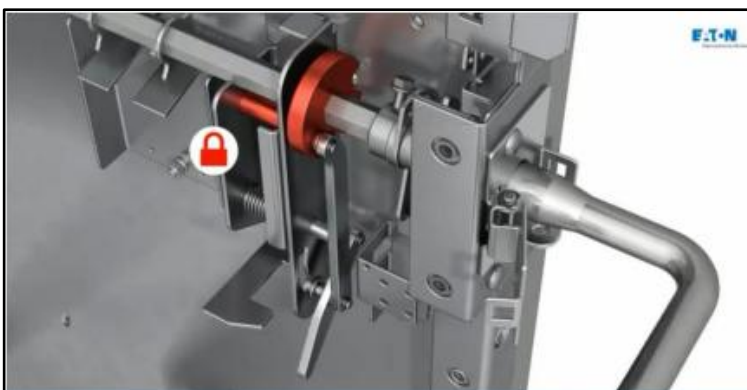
Enclavamiento mecánico – Seccionador de tierra abierto. [01]
